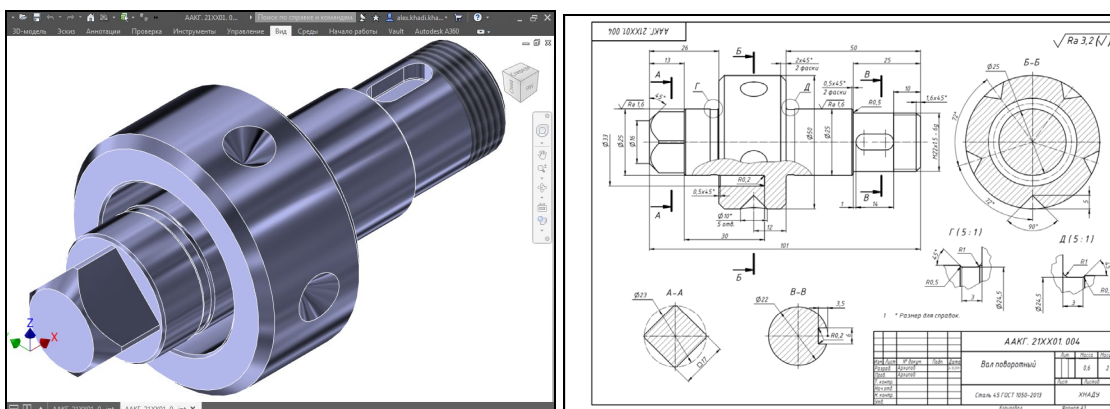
Модель та робочий кресленник деталі "Вал поворотний".
